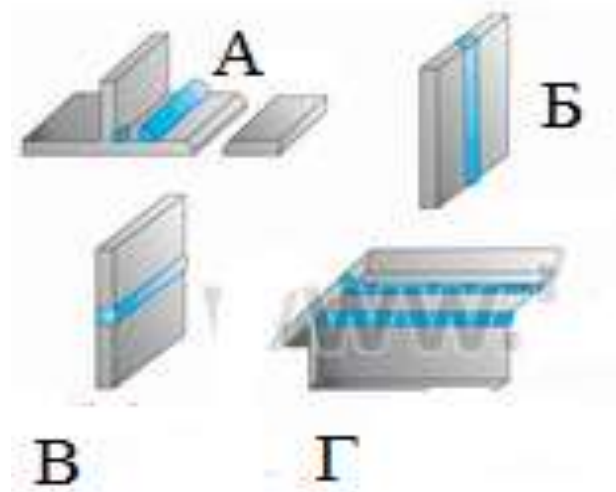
Сварные швы по положению в пространстве
